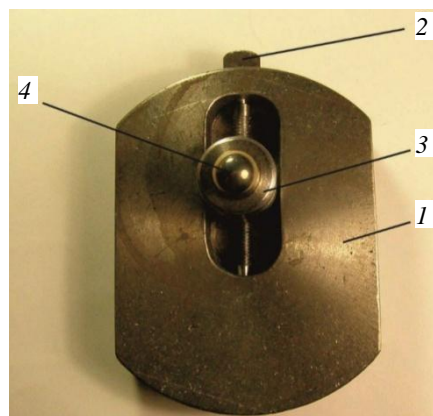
Конструкция плавающей тормозной колодки: *1* – диск; *2* – регулировочный винт; *3* – поворотная ось; *4* – шарик
